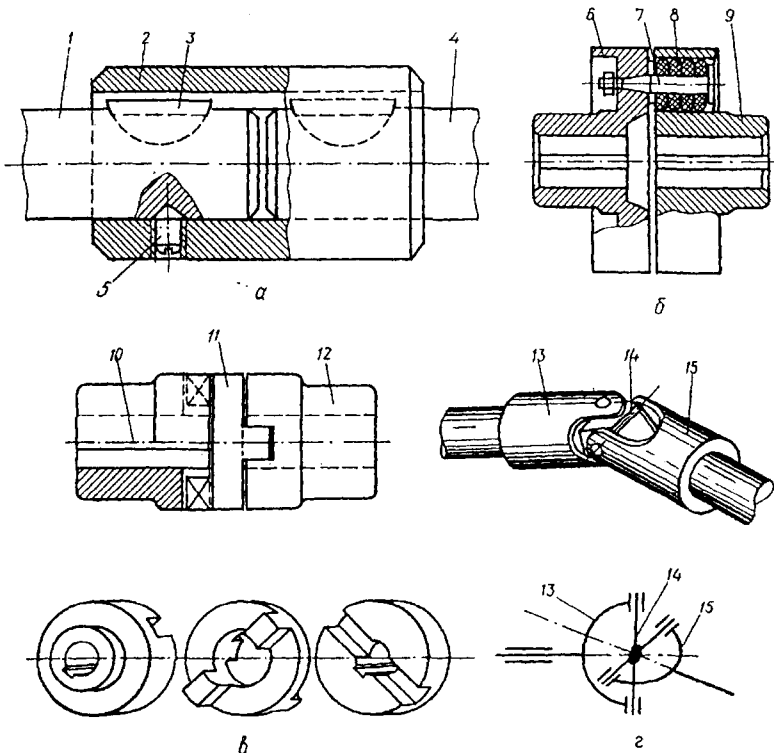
Муфты: а – втулочная; б – упругая втулочно-пальцевая; в – плавающая муфта; 1 – ведущий вал; 2 – втулка; 3 – шпонки; 4 – ведомый вал; 5 – установочный винт; 6 – левая полумуфта; 7 – палец; 8 – резиновая втулка; 10 – ось; 11 – диск; 9, 12 – правые полумуфты; 13 – левая вилка; 14 – крестовина; 15 – правая вилка
